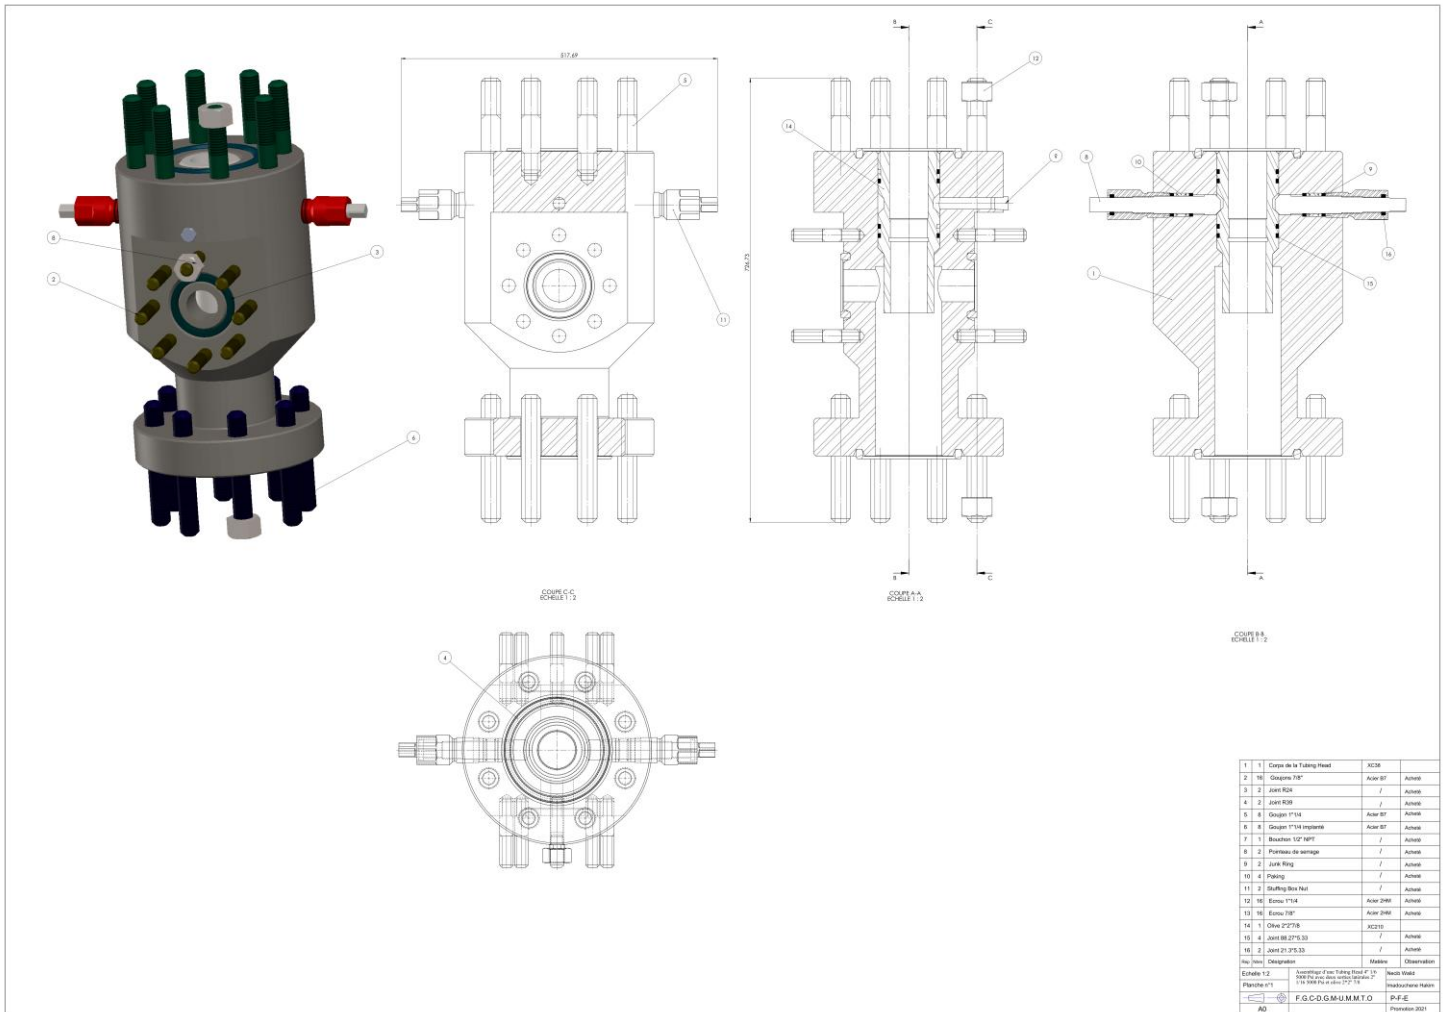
Dessin d'ensemble de la Tubing Head
